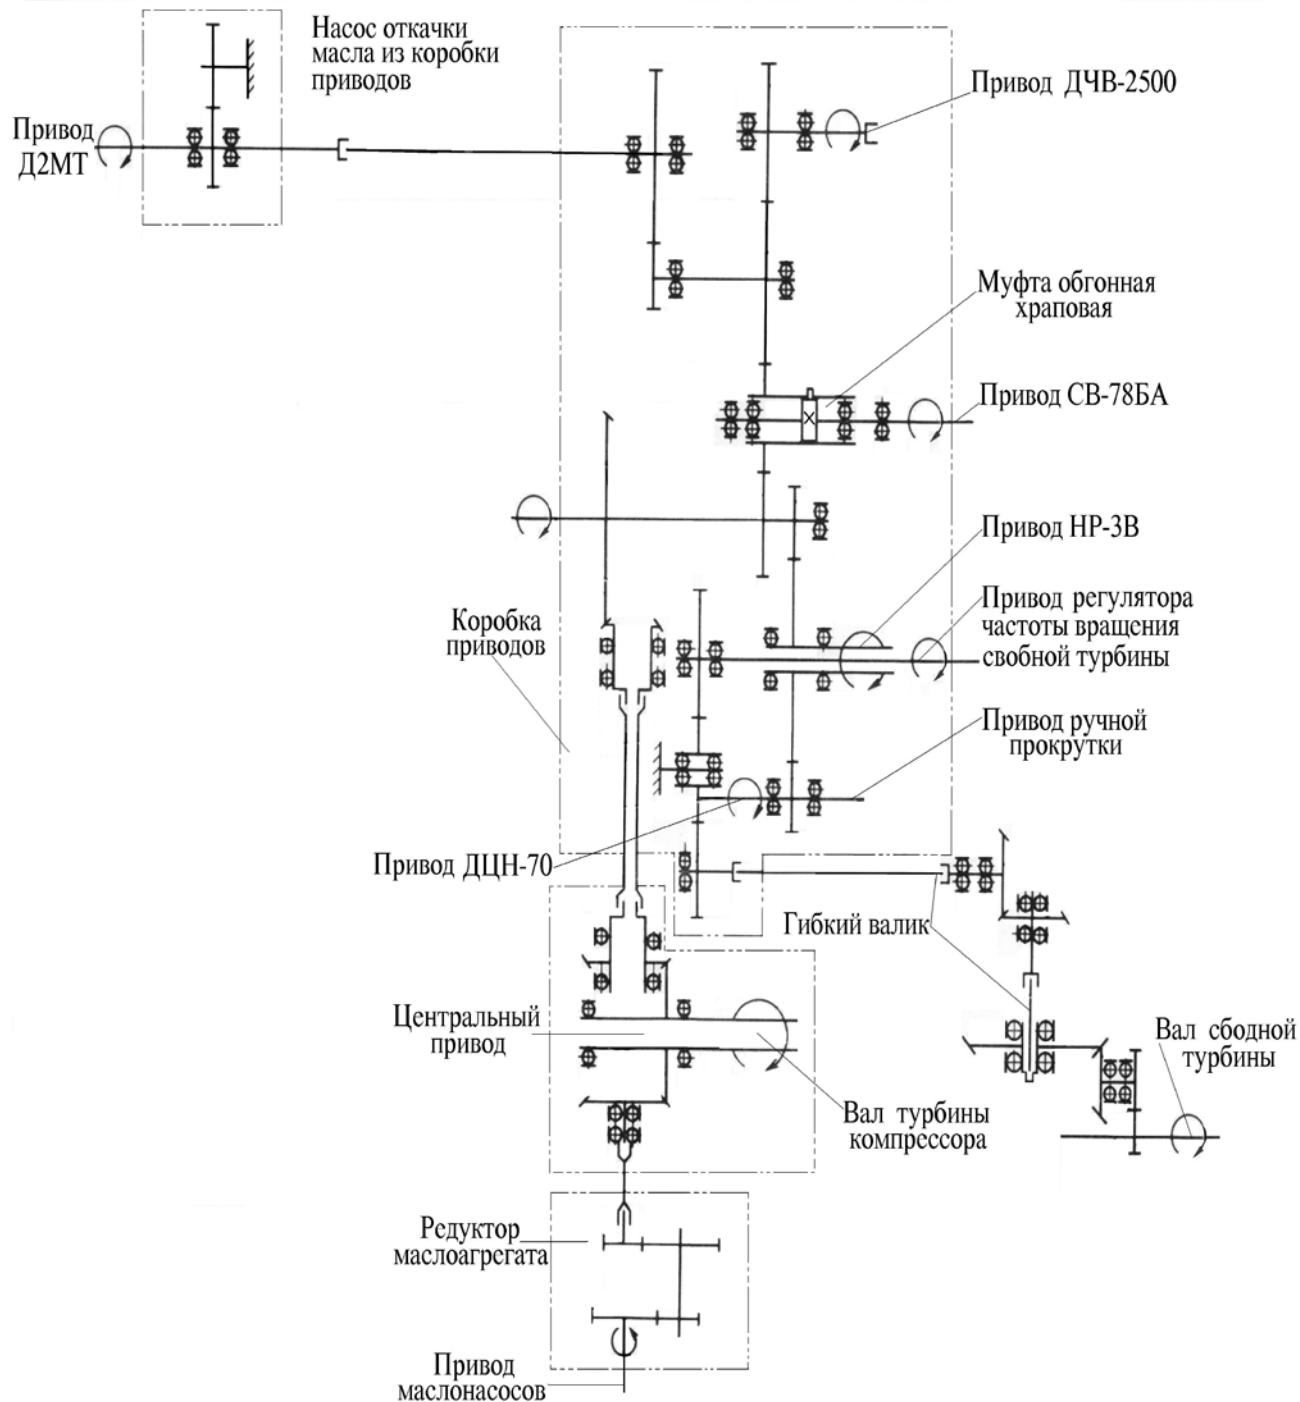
Схема приводов вспомогательных устройств двигателя.
